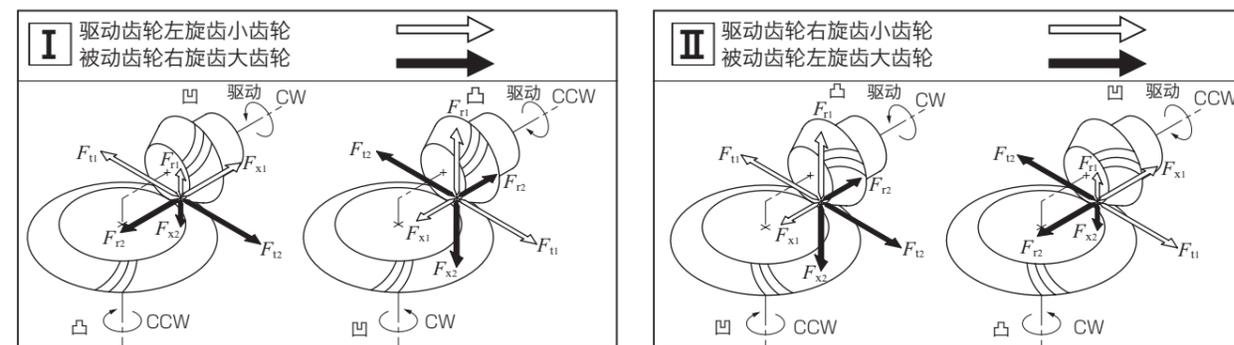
弧齿锥齿轮的旋转方向与轮齿的受力
